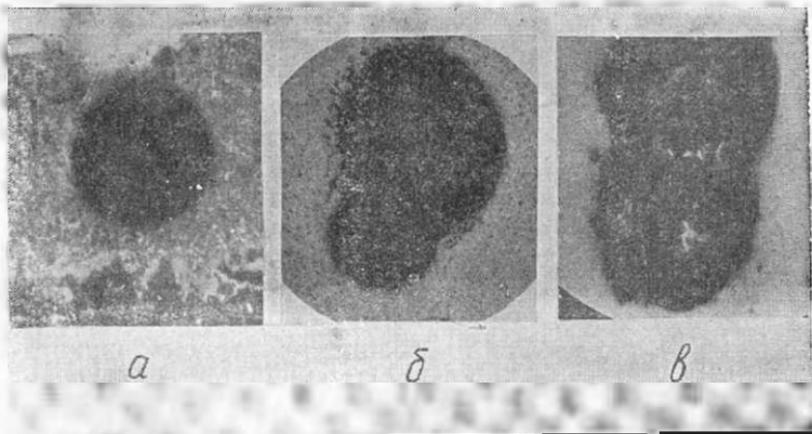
Этапы развития газовых свищей в сварных швах:
